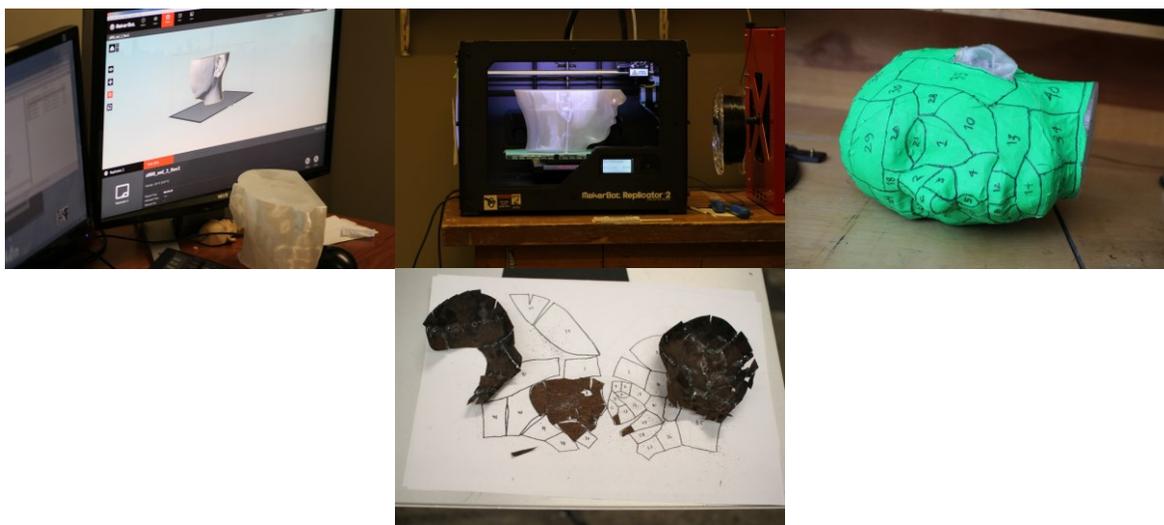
Impression 3D : guide pour le travail de soudure.
